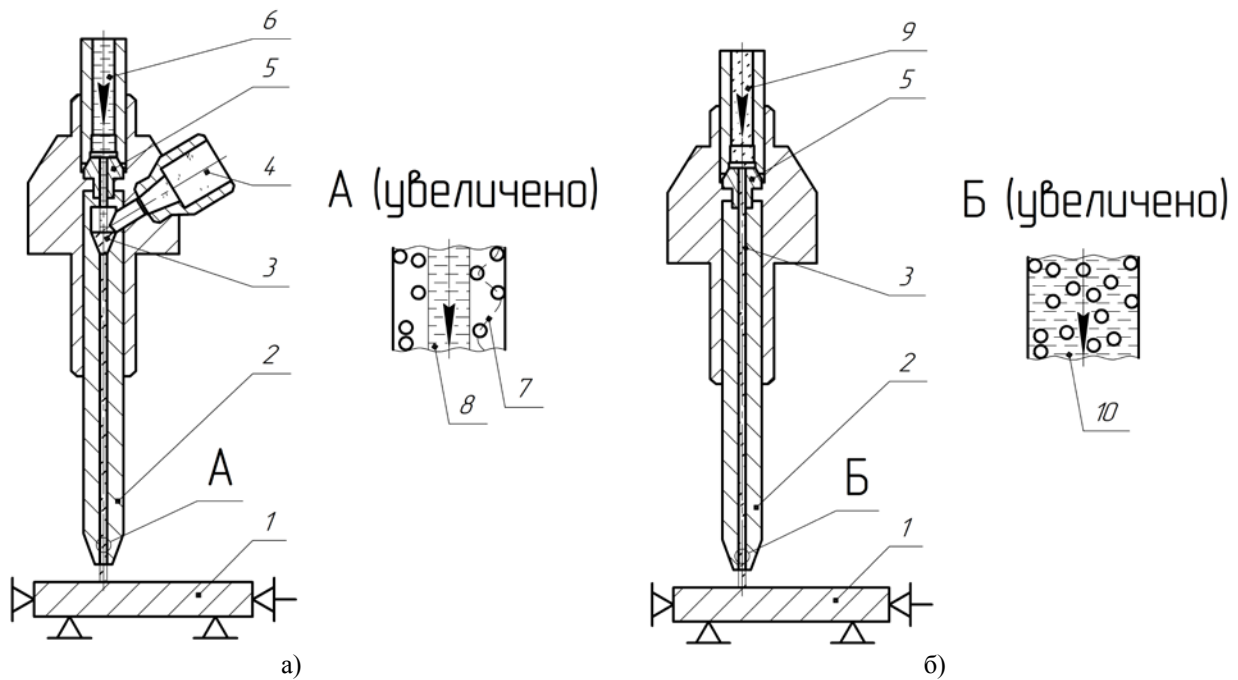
Схема головки для гидроабразивной резки: а - подача абразива в засопловую часть (ГАР); б - подача абразива в досопловую часть (ПГАР); 1 - обрабатываемая заготовка; 2 - струеформирующая трубка; 3 - узел смешивания; 4 - канал подвода абразивного порошка; 5 - гидроструйное сопло; 6 - подвод воды под давлением; 7 - приблизительная траектория абразивной частицы; 8 - струя воды; 9 - подвод абразивно-жидкостной суспензии; 10 - режущая струя абразивно-жидкостной суспензии
